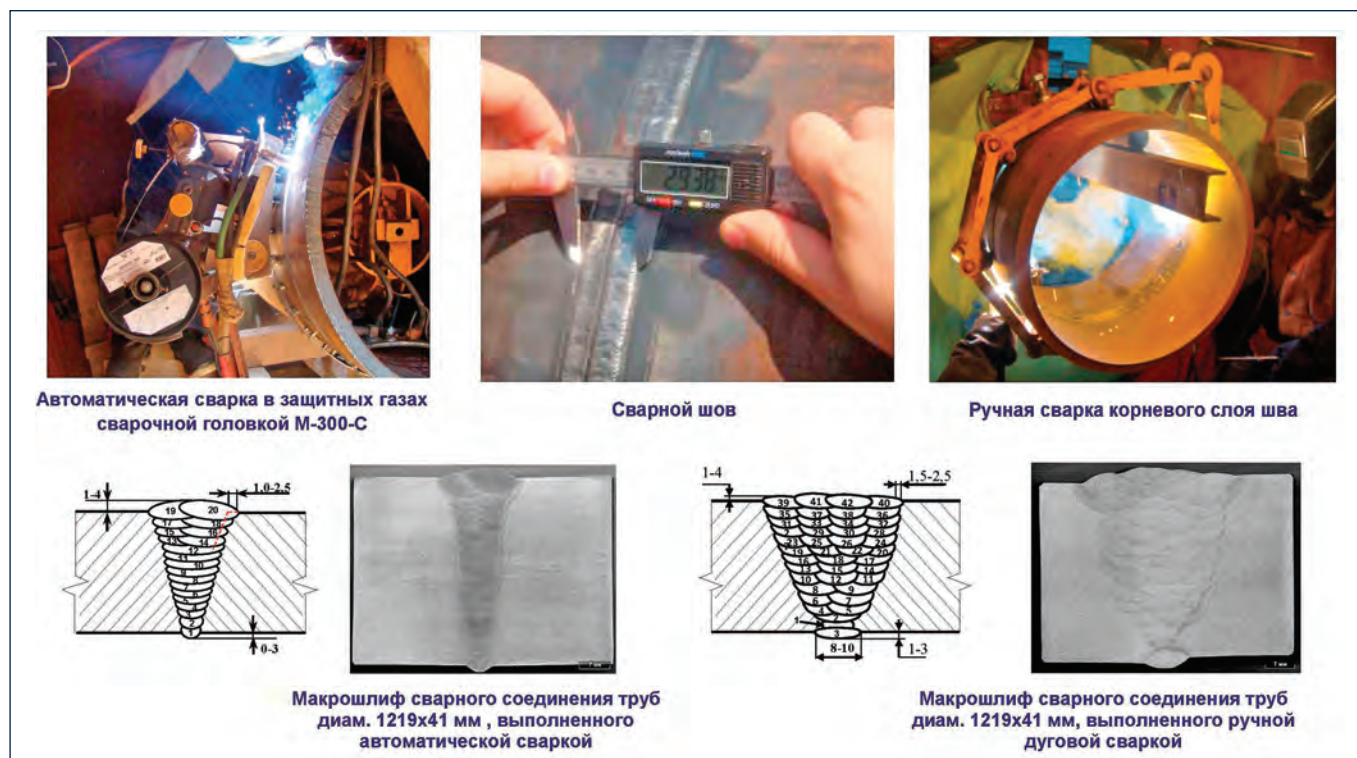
Геометрические параметры разделки торцов кромок труб и сварного шва (в сравнении по способам сварки)
